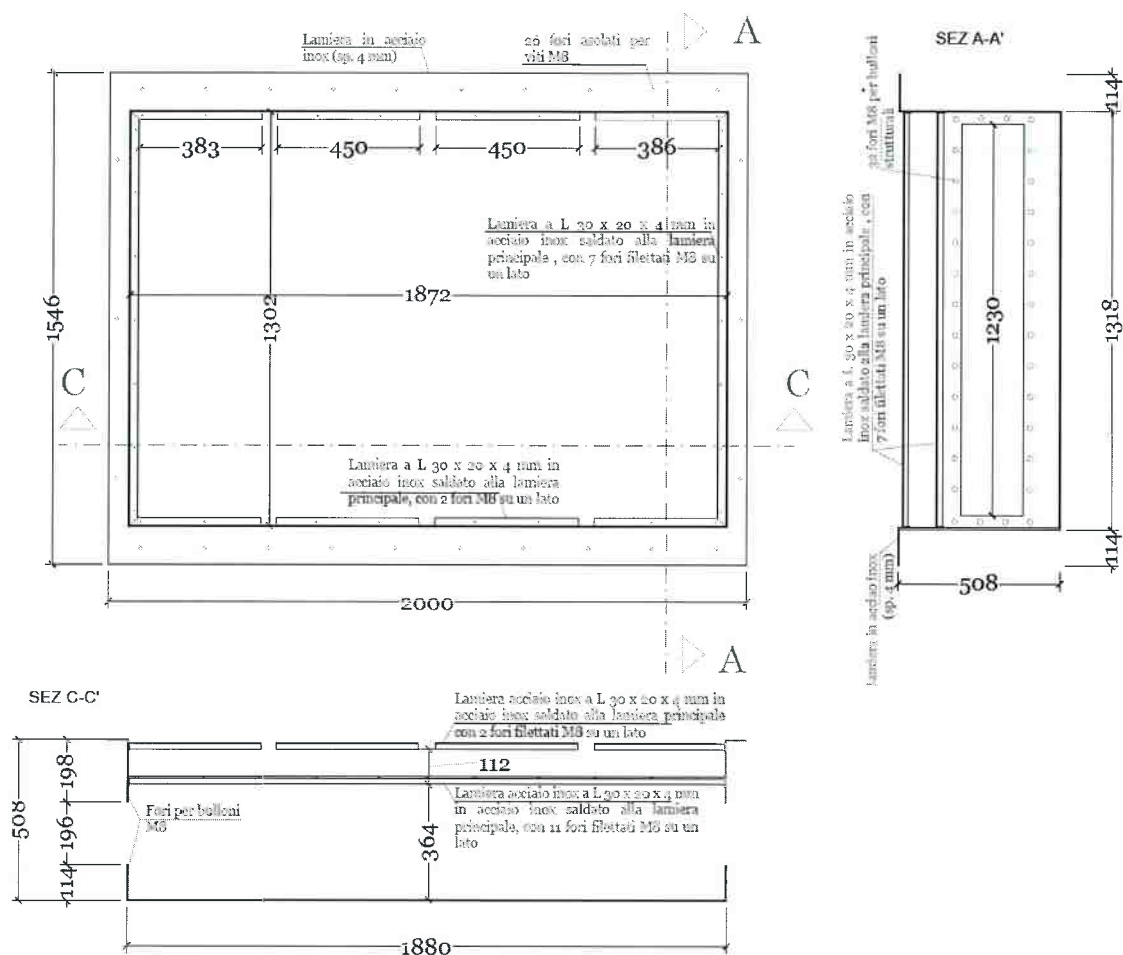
Vista in pianta e sezioni dell'elemento costruttivo: Vasca tipo 1
